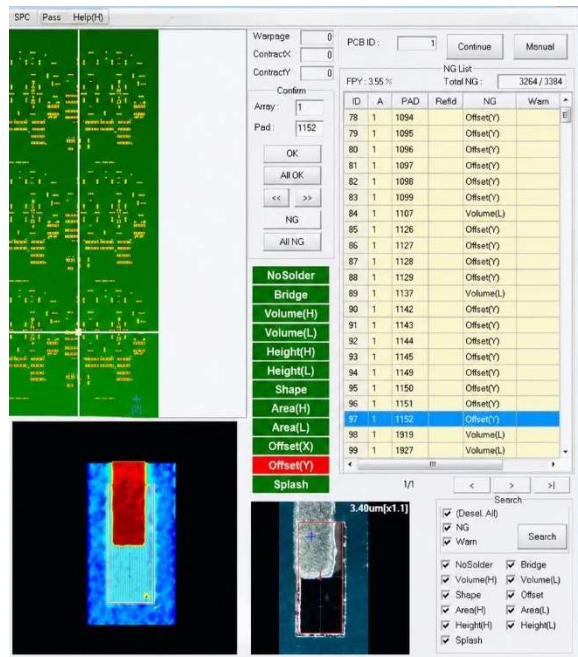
Desplazamiento de soldadura detectada en SPI.
